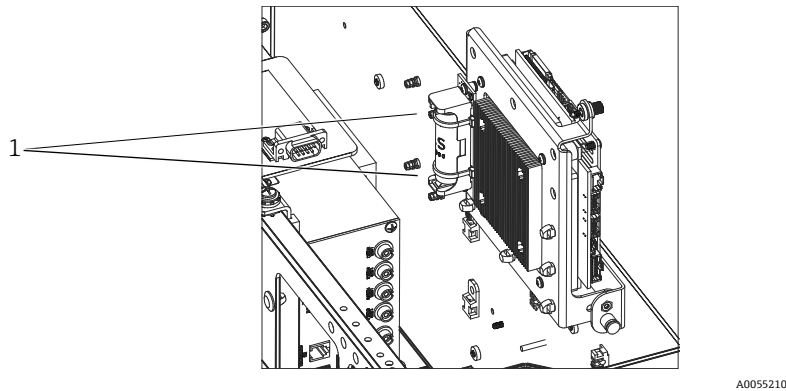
Kabelbinder (1), mit denen die Batterie gehalten wird, entfernen
